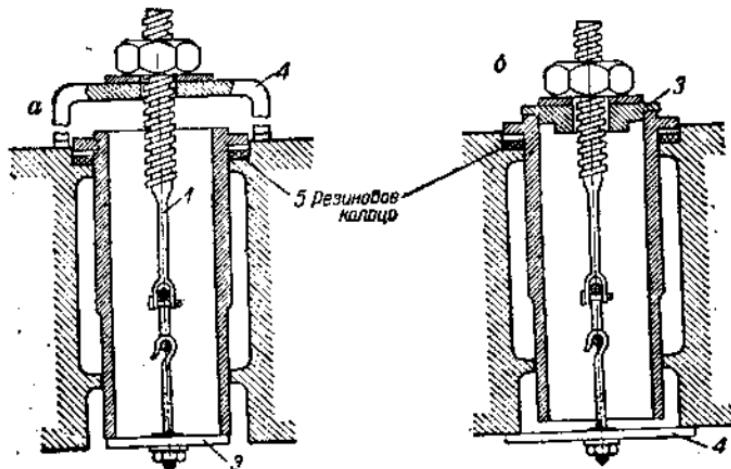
Устройство для выпрессовки (а) и запрессовки (б) гильз.
